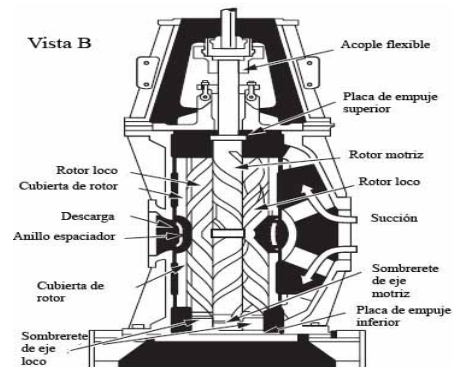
Partes de una bomba rotativa de tornillo seccionada
